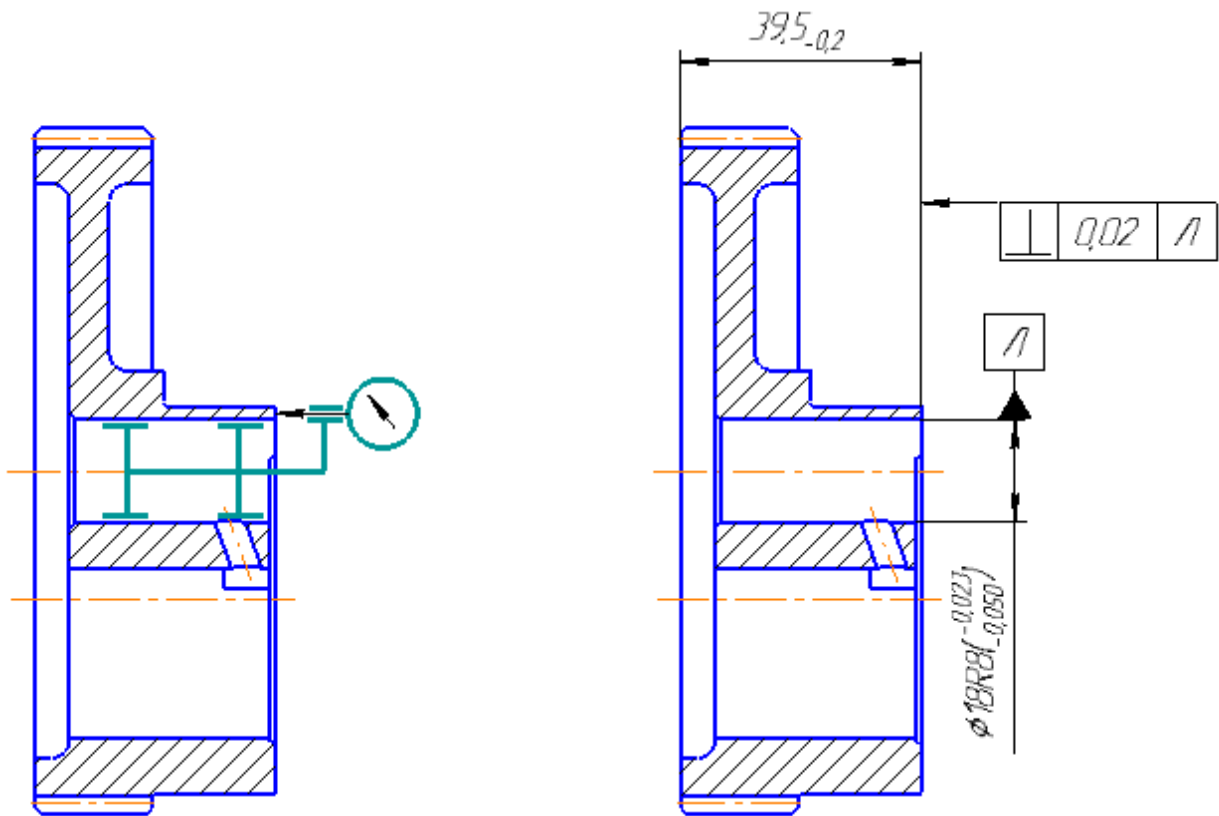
Контрольований параметр деталі і схема контролю
